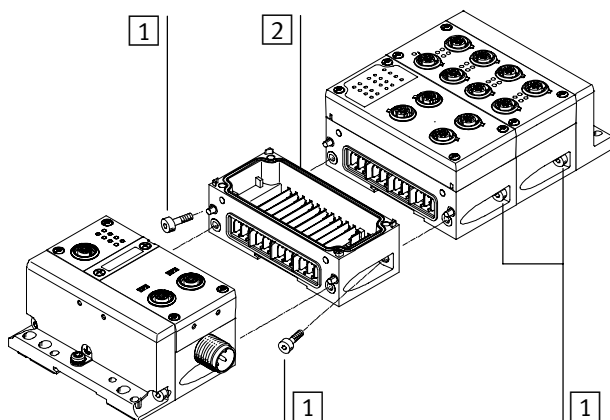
/10: CPX-Terminal mit Anschlussblöcken und Verkettungsblöcken in Metallausführung
